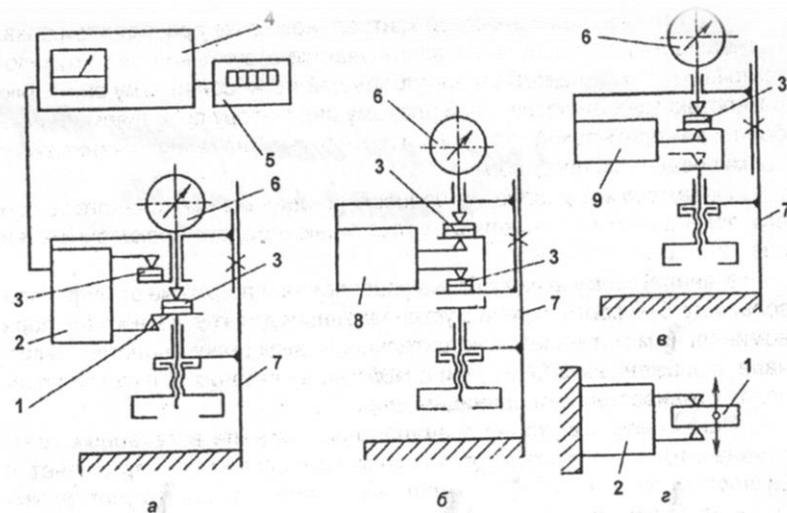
Схема проверки, настройки и калибровки измерительных преобразователей
